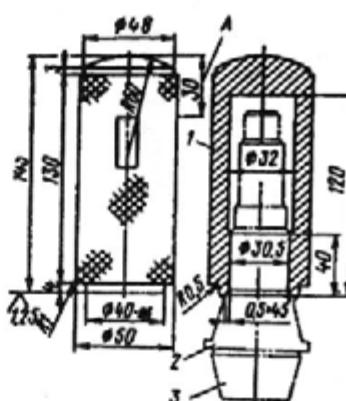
Оправка для напрессовки внутреннего кольца заднего подшипника на вал ведущей шестерни главной передачи:
